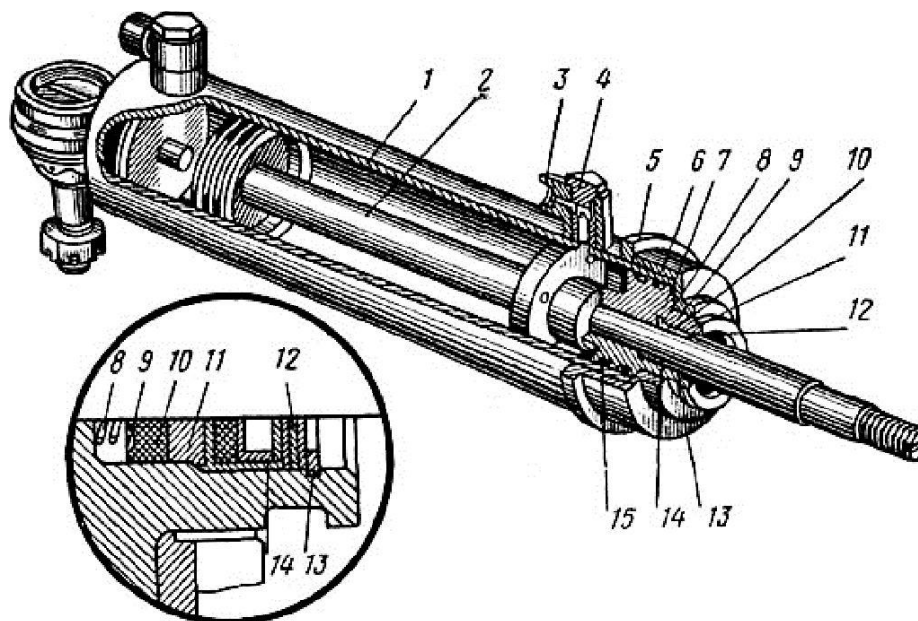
Силовой цилиндр усилителя автомобиля ГАЗ-66:
